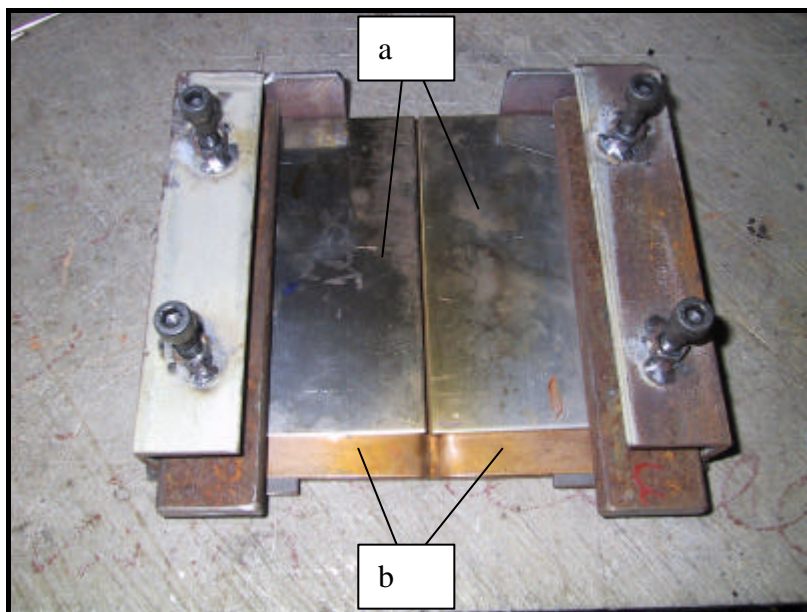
Corpo de prova e gabarito para soldagem – Antes da soldagem.
